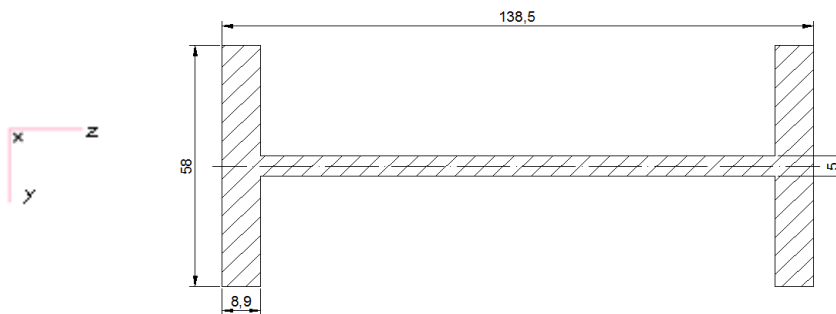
sección en la unión soldada de la pata 2( $45^\circ$ )
